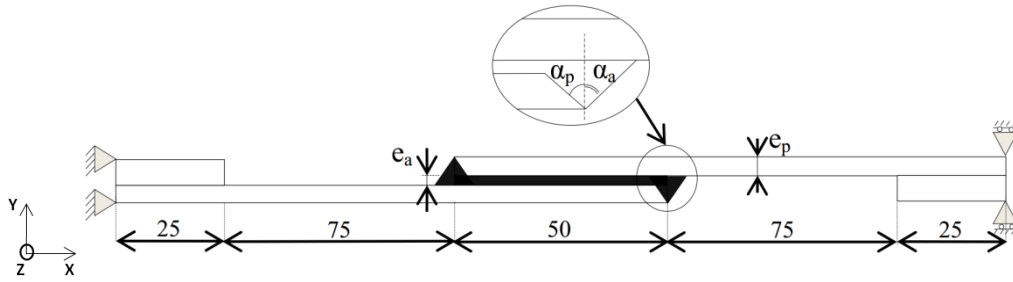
modèle géométrique de l'assemblage à simple recouvrement (dimensions en mm).
